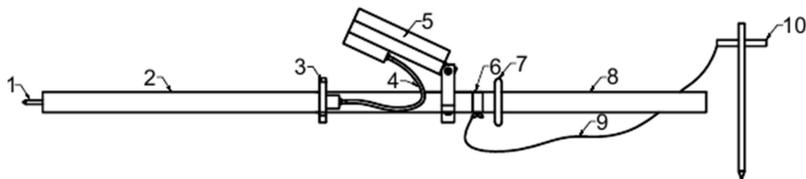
Внешний вид штанги-измерителя напряжения прикосновения ШИП-5:
